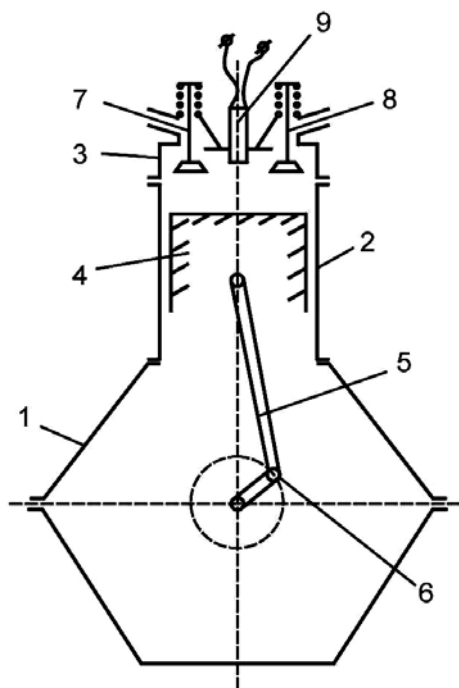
Схема простейшего одноцилиндрового двигателя с принудительным воспламенением топливовоздушной смеси: 1 – картер; 2 – цилиндр; 3 – головка цилиндра; 4 – поршень; 5 – шатун; 6 – коленчатый вал; 7 – впускной клапан; 8 – выпускной клапан; 9 – свеча зажигания
